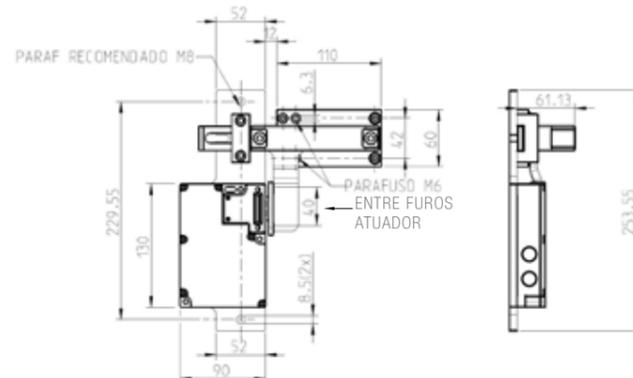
Dimensões de montagem do trinco AZM 161
